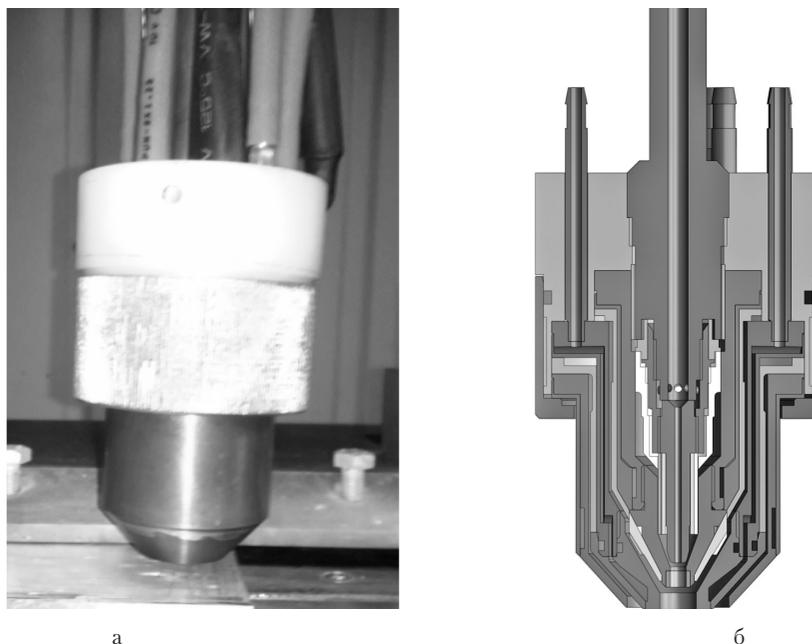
Внешний вид (а) и поперечный разрез (б) компьютерной модели горелки для гибридной плазменной сварки плавящимся электродом
